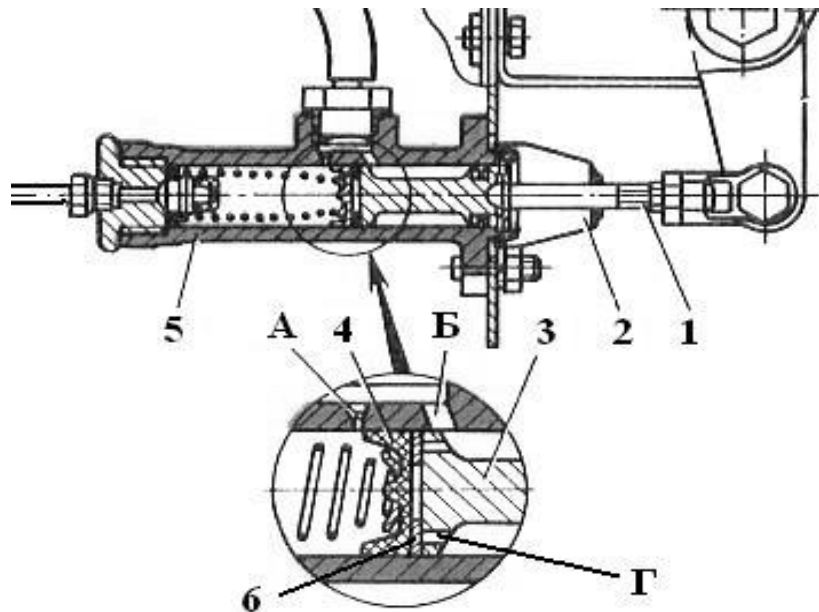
Главный цилиндр гидропривода выключения сцепления автомобилей ГАЗ:
